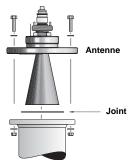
Installation de l'antenne cône à raccords de rincage sur le piguage
